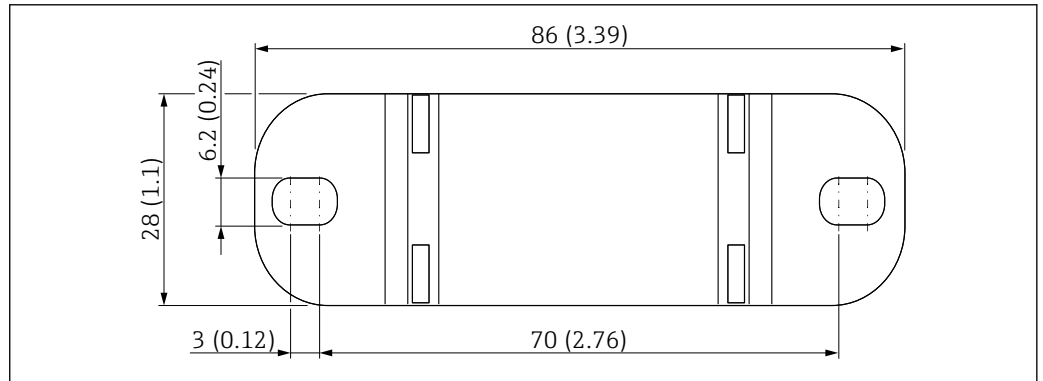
Visión general de la placa de montaje en pared. Unidad de medida mm (in)
